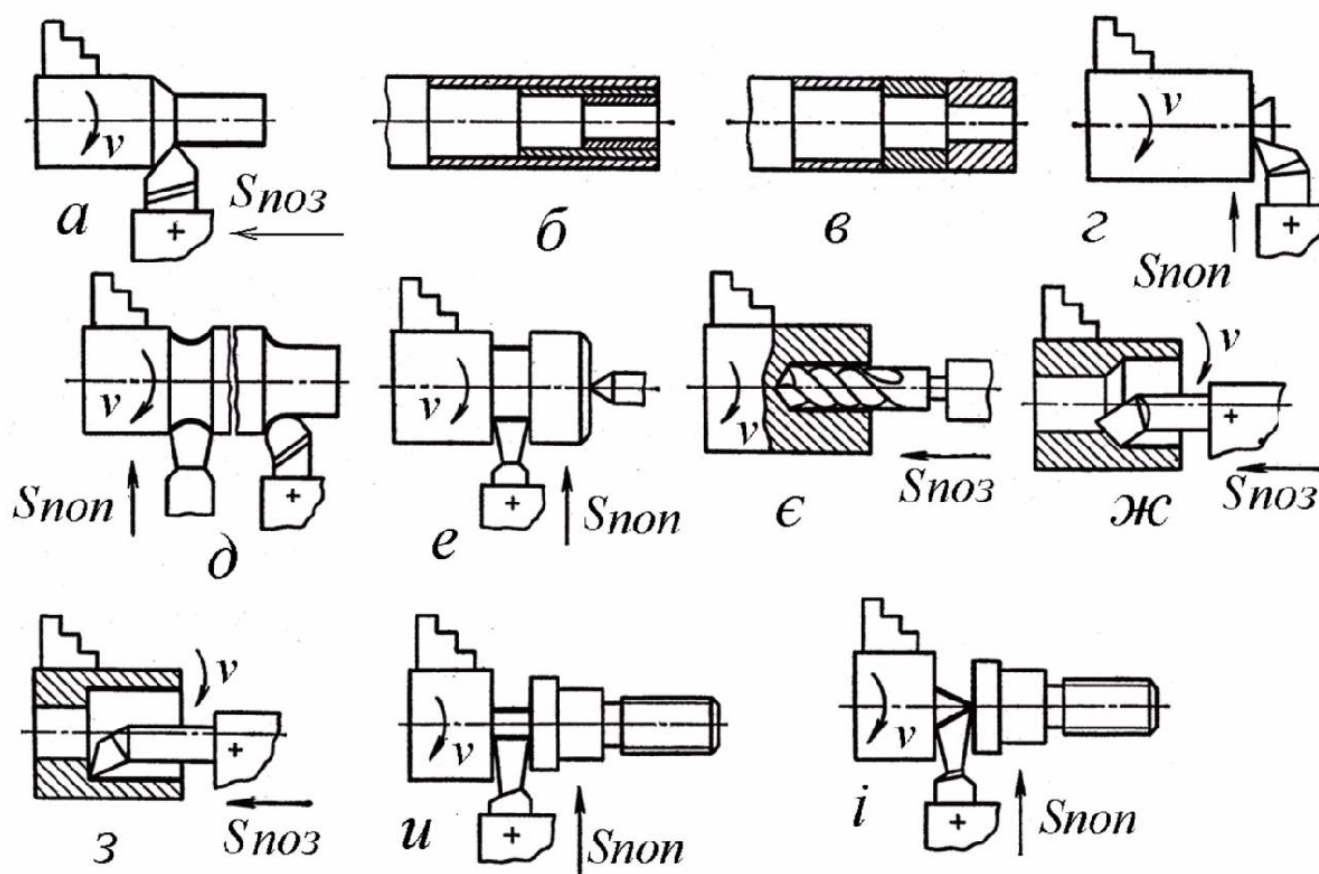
Схеми обробки заготовок на токарно-гвинторізному верстаті
